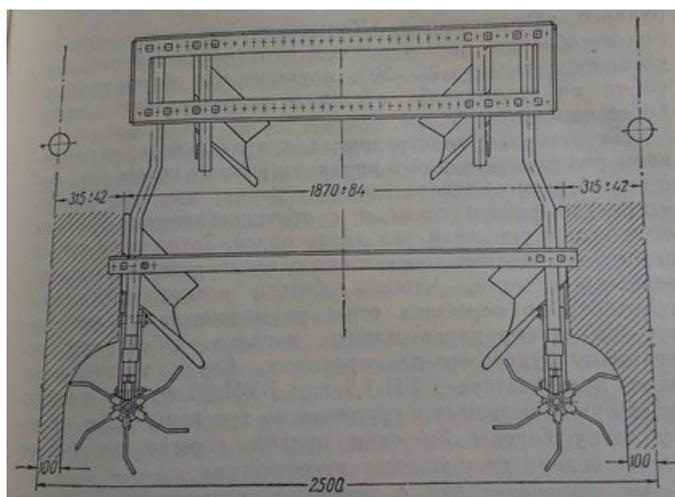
Схема плуга ВУМ-60 с приспособлением для открывки лоз
